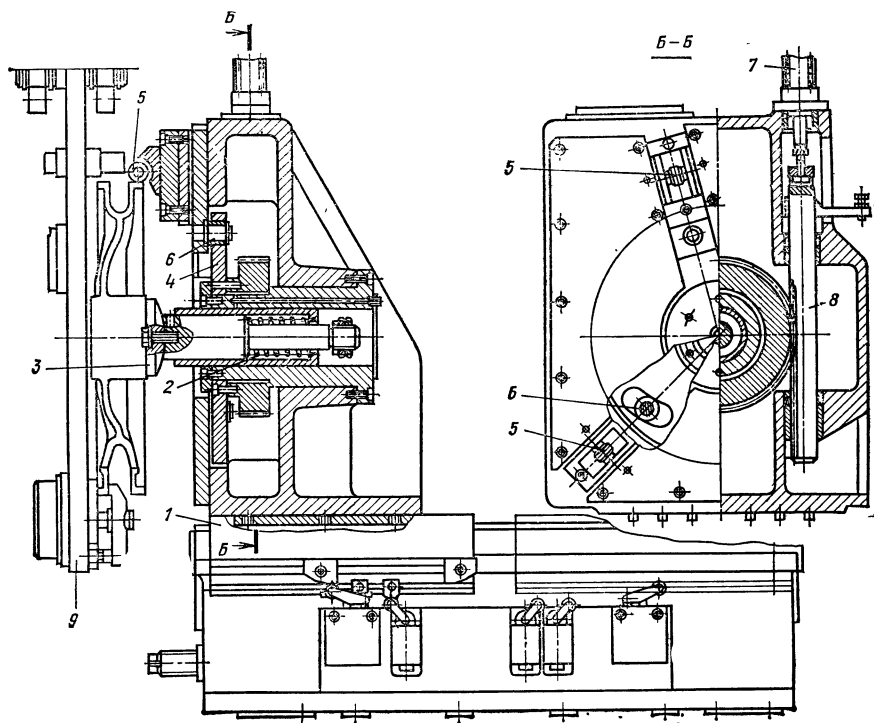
Механизм центрирования детали в приспособлении-спутнике:
